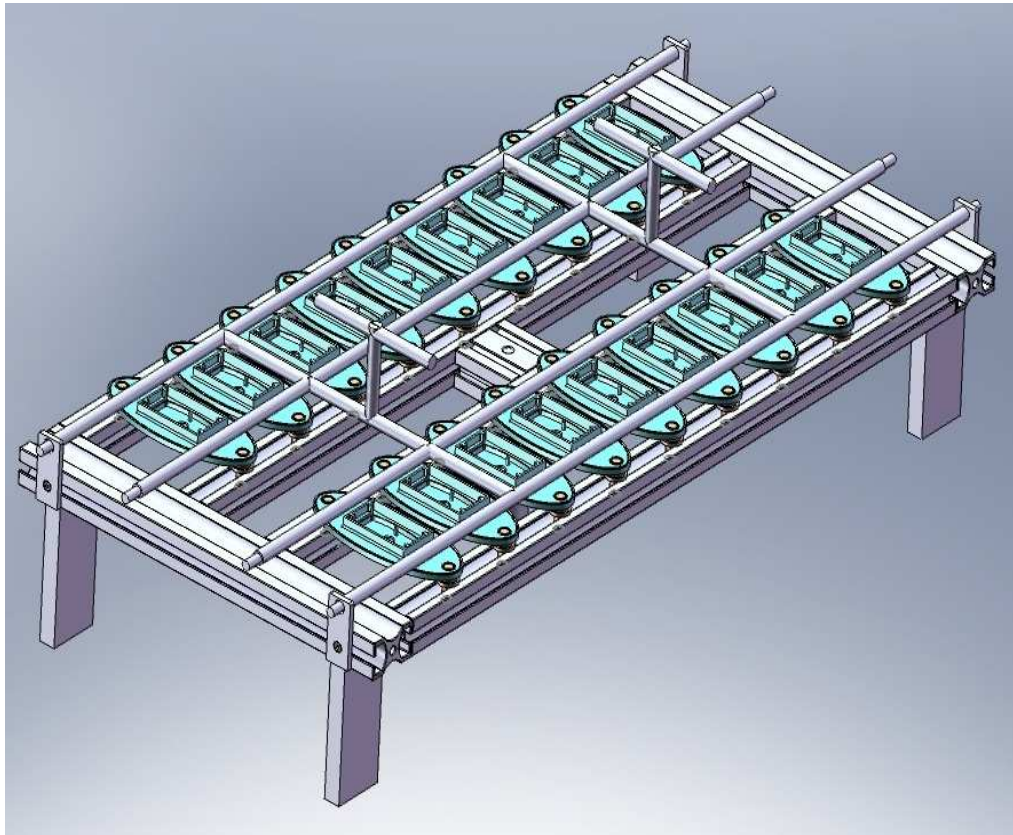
Assembly gabarit psi (c/ cablagem)
